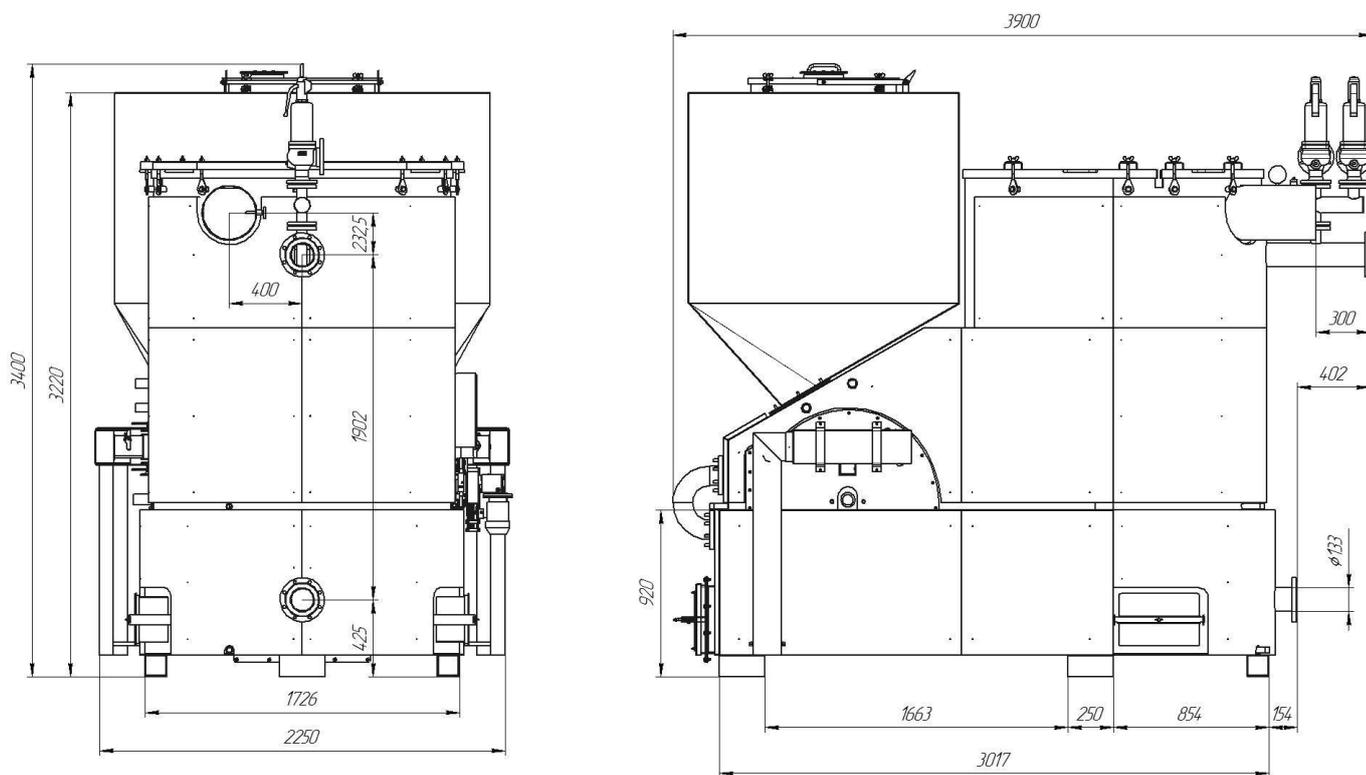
Эскизы котла Прометей-Автомат-1000М с габаритными размерами
